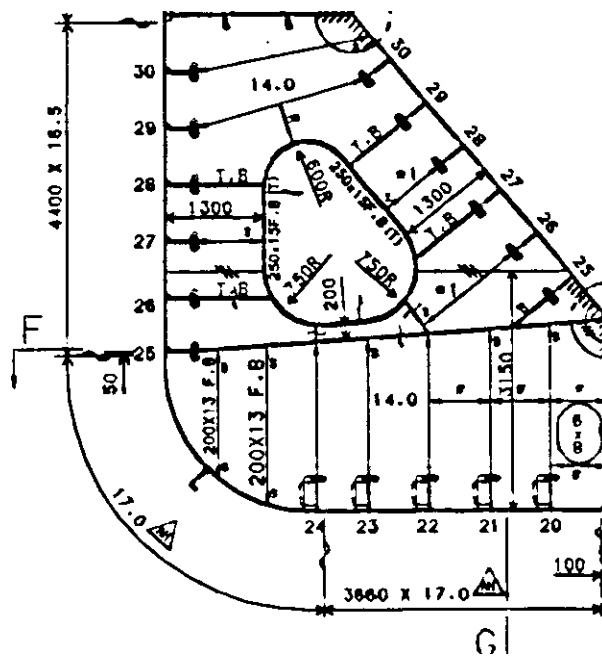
Εγκάρσια διατομή του πλοίου (Web Section).
